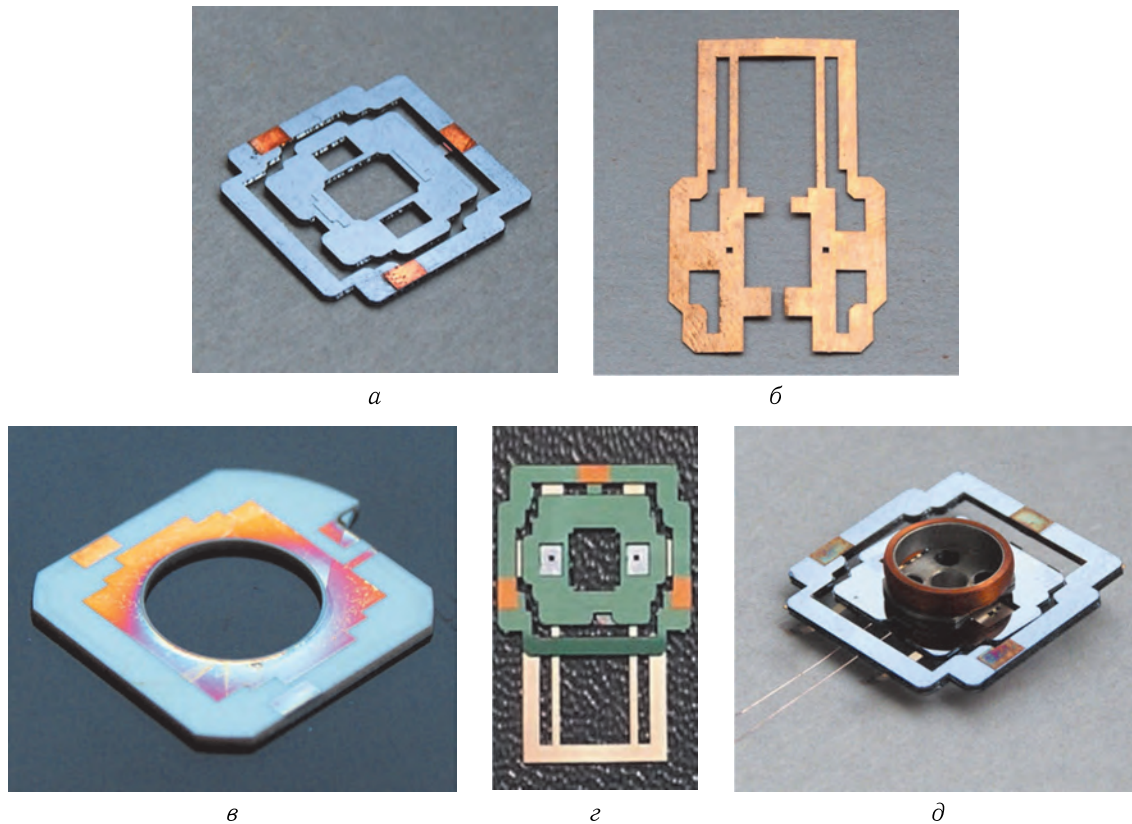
Фотографии изготовленных образцов ЧЭ акселерометра: *а* — полумаятник; *б* — упругая перемычка; *в* — ситалловая статорная пластина; *г* — маятниковый подвижный узел (заготовка); *д* — маятниковый подвижный узел (сборка)
